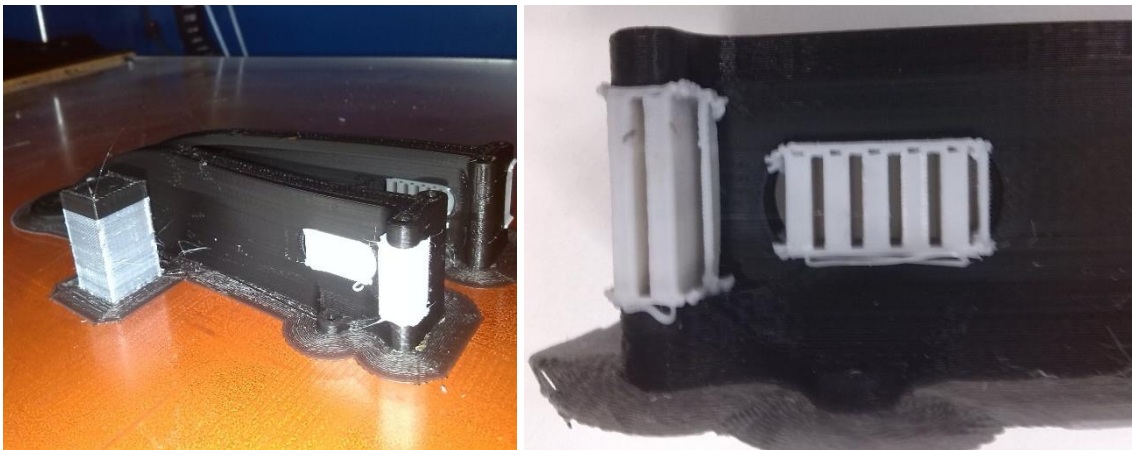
Componentes fabricados (izquierda). Detalle del material de soporte (derecha).
